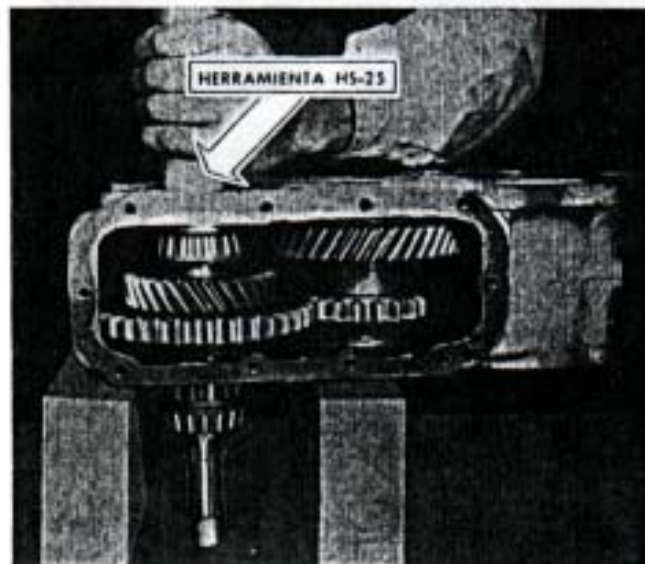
Instalando el cono del cojinete a rodillos delantero, con la herramienta HS-25.
